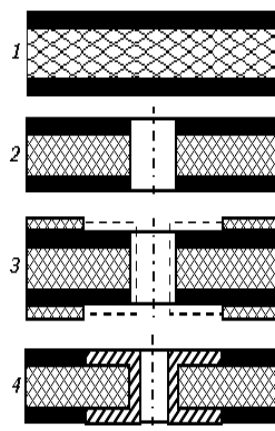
Схема процесса изготовления печатных плат полуаддитивным методом:
